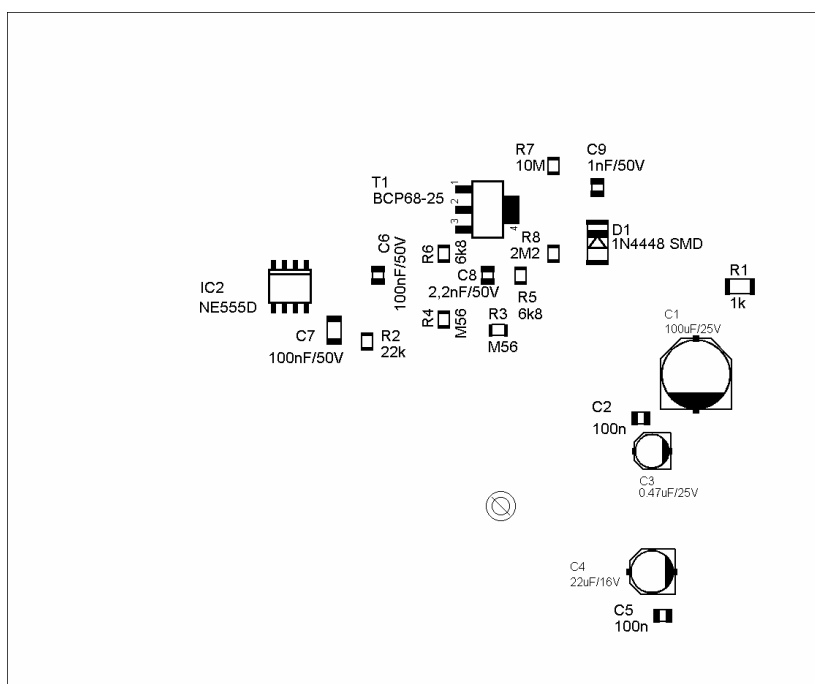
Motiv plošného spoje desky napájení a měření bottom
